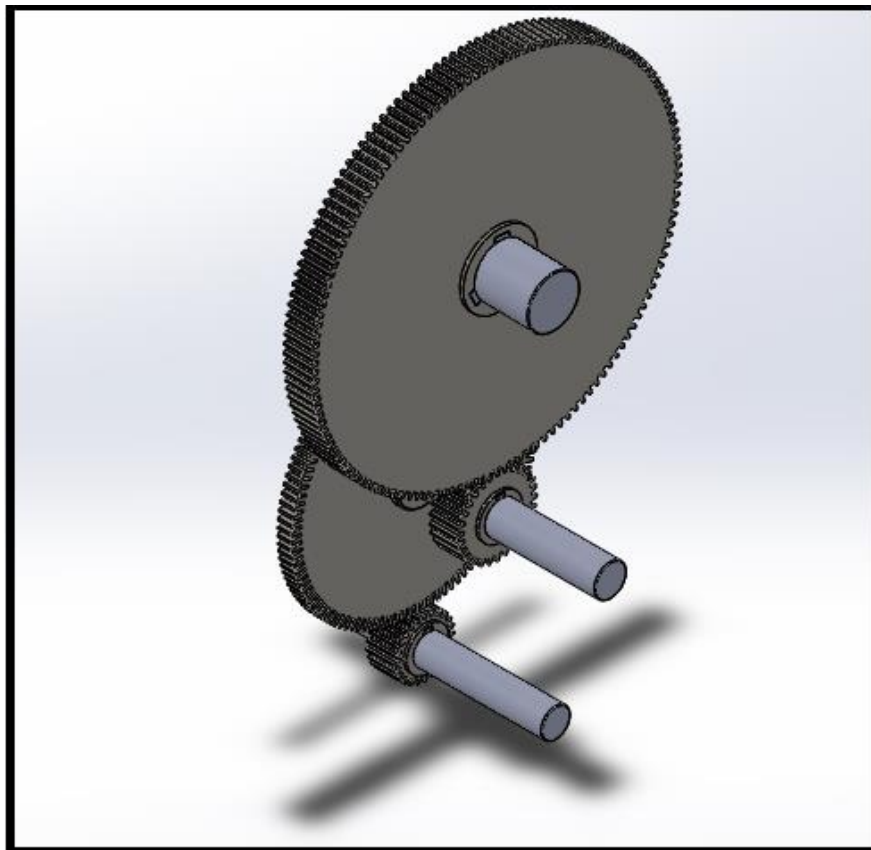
Montagem dos elementos internos do redutor, vista isométrica.(Autor, 2022)
